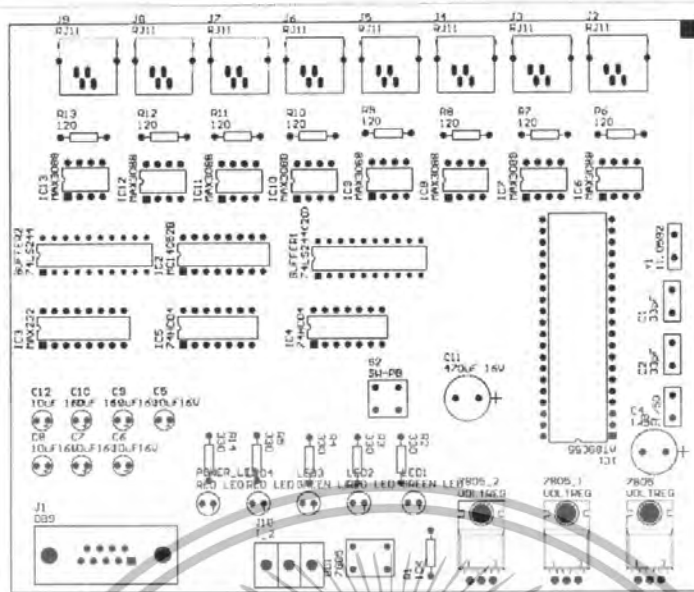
แสดง PCB Top Layer ของ Switch of Spot
